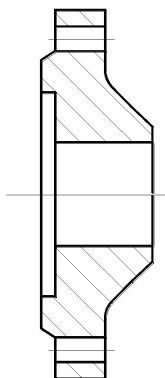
Конструкции фланцев стальных плоских приварных
